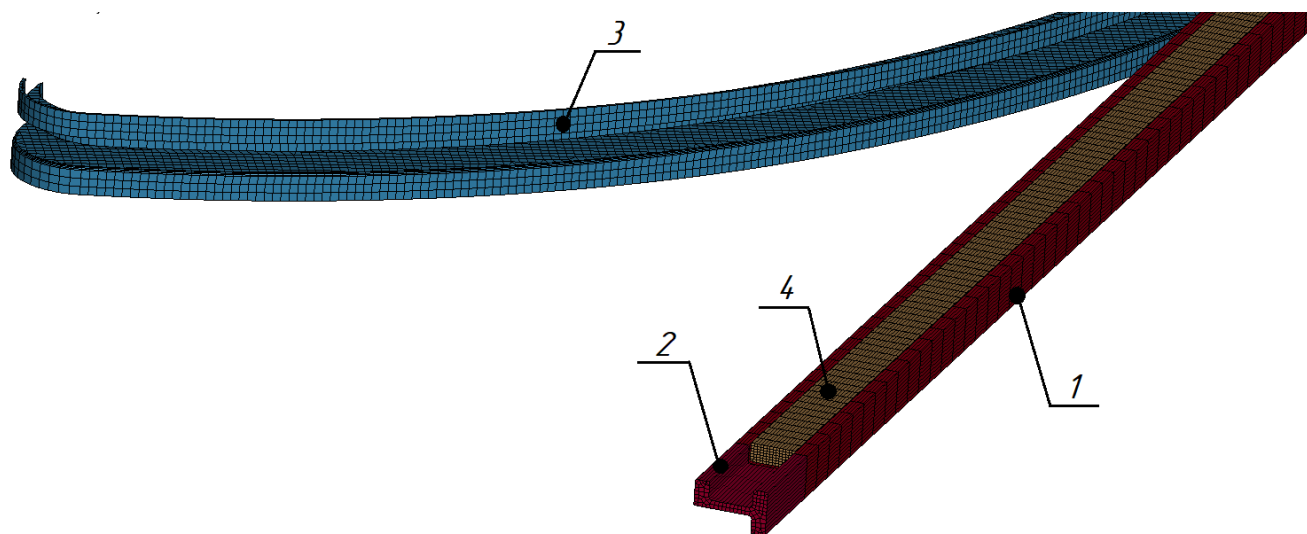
Модель гибки с растяжением профильной заготовки по формообразующей оправке: 1 – деформируемая часть заготовки; 2 – часть заготовки, находящаяся в зажимах гибочно-растяжного прессы; 3 – формообразующая оправка, 4 – полиуретановая вставка
